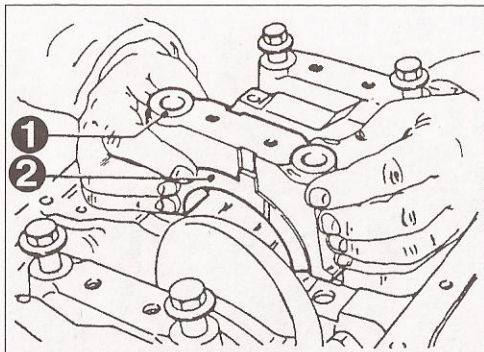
Установка крышки подшипника, определяющего боковой зазор коленчатого вала.
